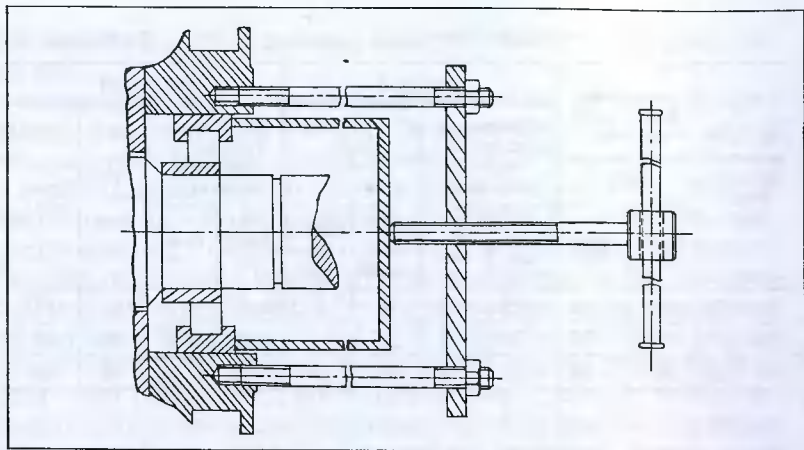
Приспособление для установки наружного кольца роликоподшипника типа 32000
